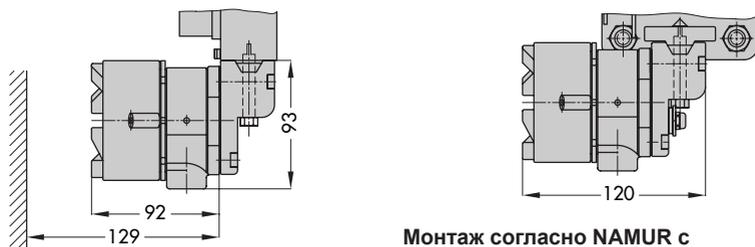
Габаритные чертежи для исполнений с литой или стержневой рамой
